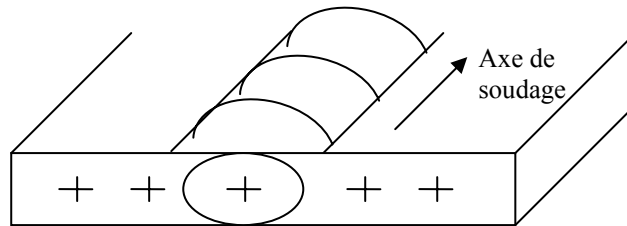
Profil de dureté à mi-épaisseur de tôle, perpendiculairement à l'axe de soudage,
